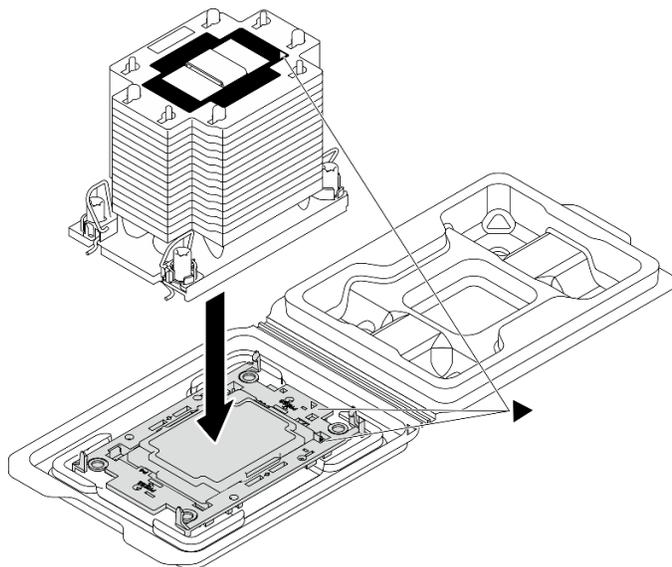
Assemblage du module de processeur-dissipateur thermique avec le processeur dans le plateau d'expédition
